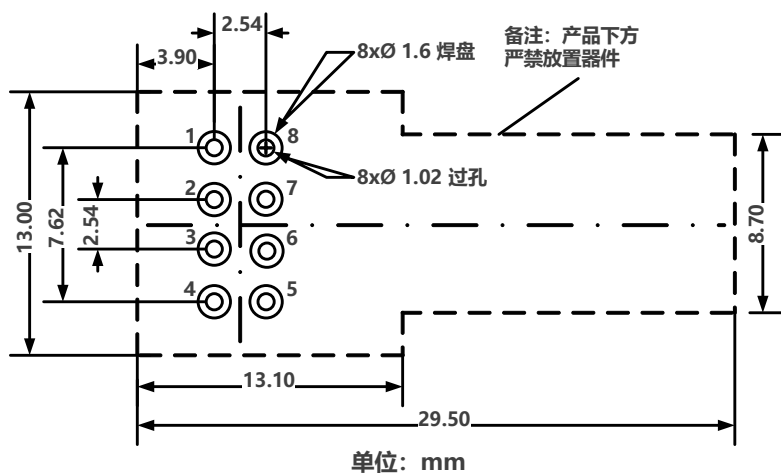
PCB Layout 设计推荐尺寸图（俯视图）
